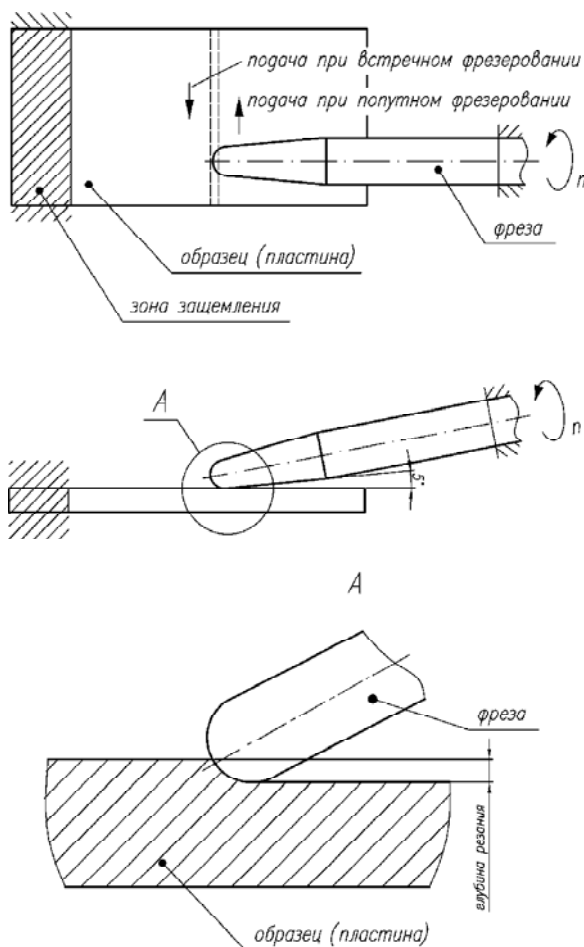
Схема высокоскоростного чистового фрезерования пластины
